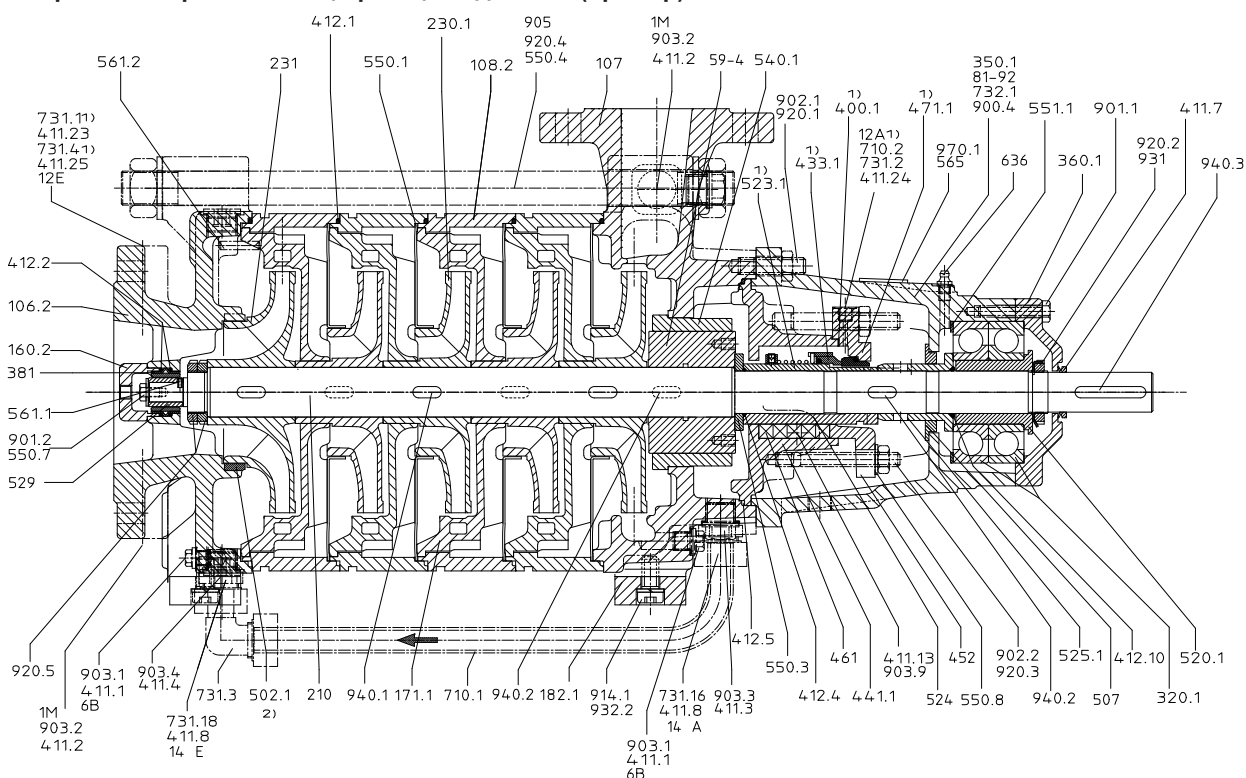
Multitec - тип установки А - типоразмер 65-100
